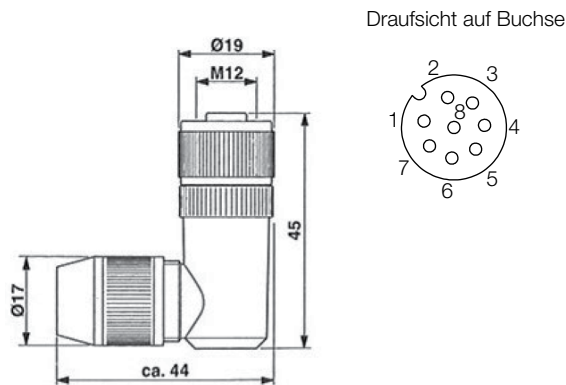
Steckverbinder BCC M488-0000-1A-000-43x834-000
